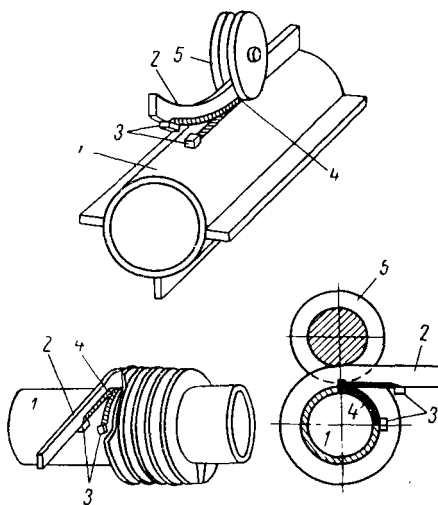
Приварка ребер к трубам с помощью контактной сварки токами ВЧ:
